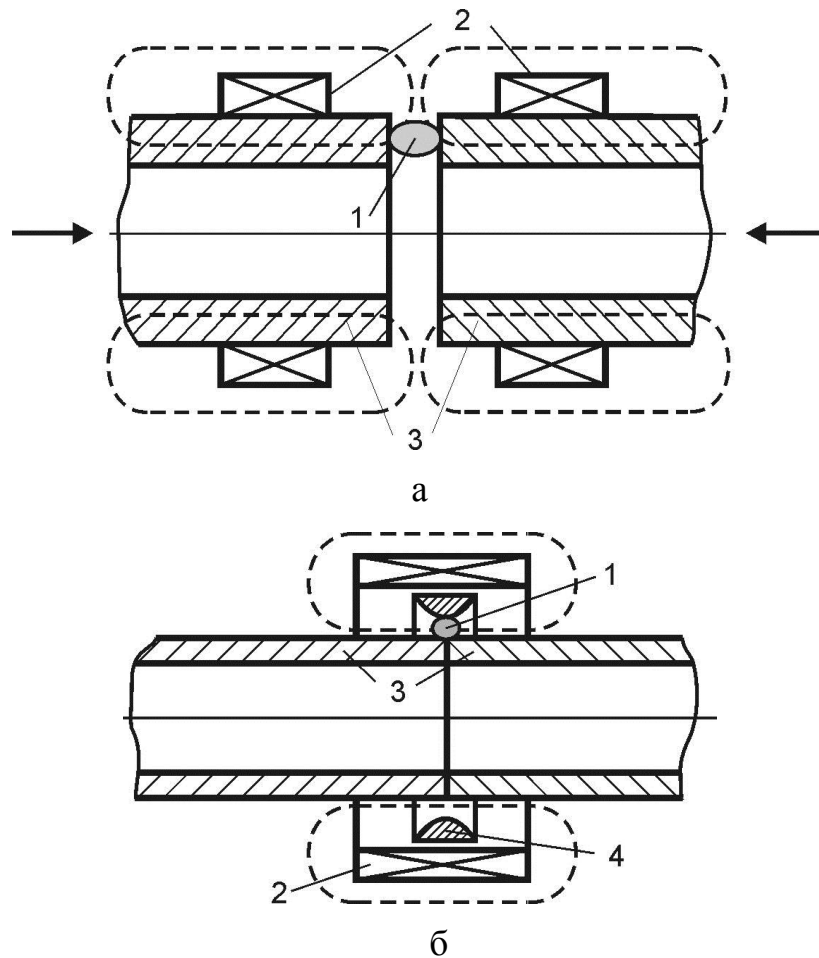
Принципиальные схемы сварки дугой, управляемой магнитным полем: 1 – электрическая дуга; 2 – устройства создания магнитного поля; 3 – свариваемые детали; 4 – вспомогательный электрод
